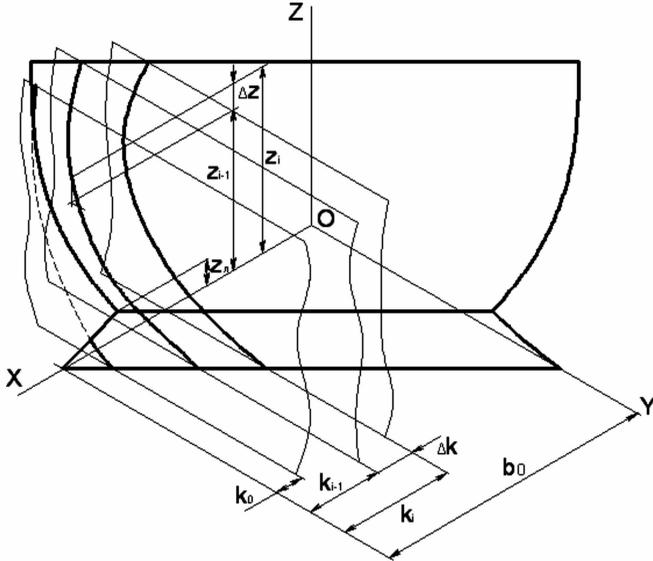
Схема образования рабочей поверхности плужного корпуса
